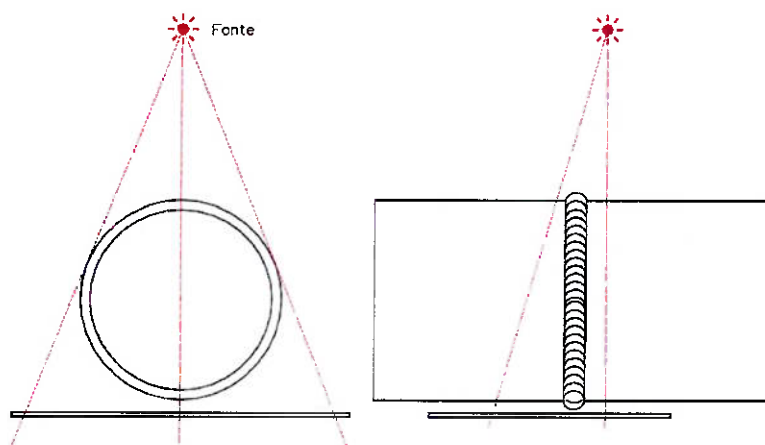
Técnica de exposição Parede Dupla – Vista Dupla.
